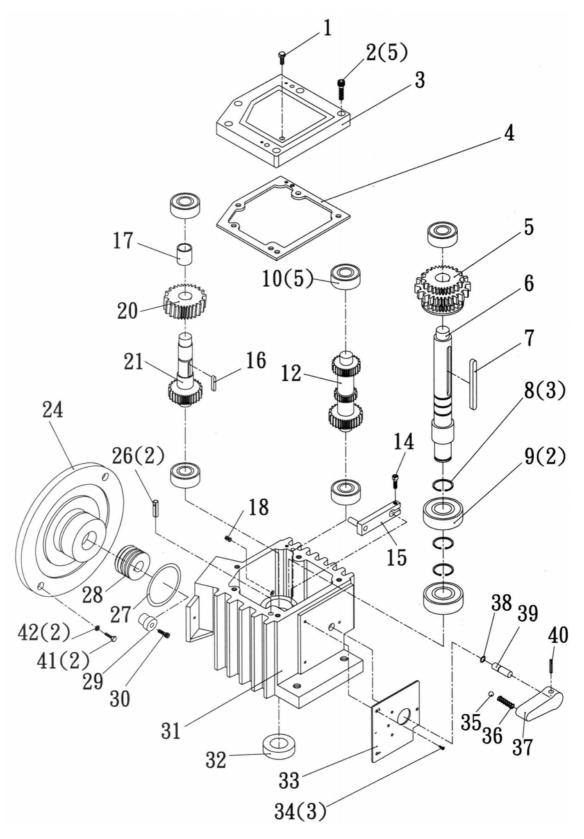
Explosionszeichnung Getriebe - Explosion drawing gear: 712AGN second generation
